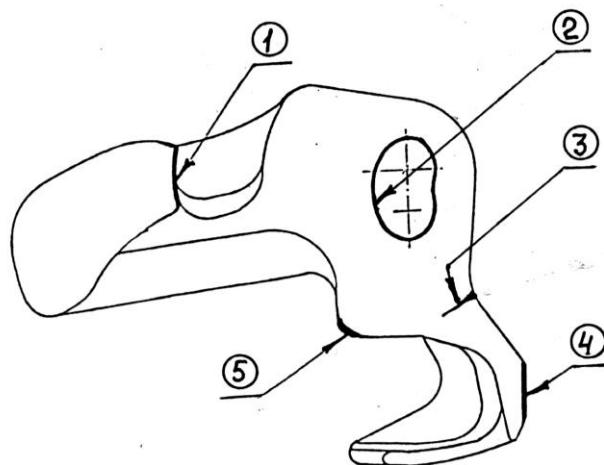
Дефекты замкодержателя автосцепки, ремонтируемые сваркой или наплавкой
